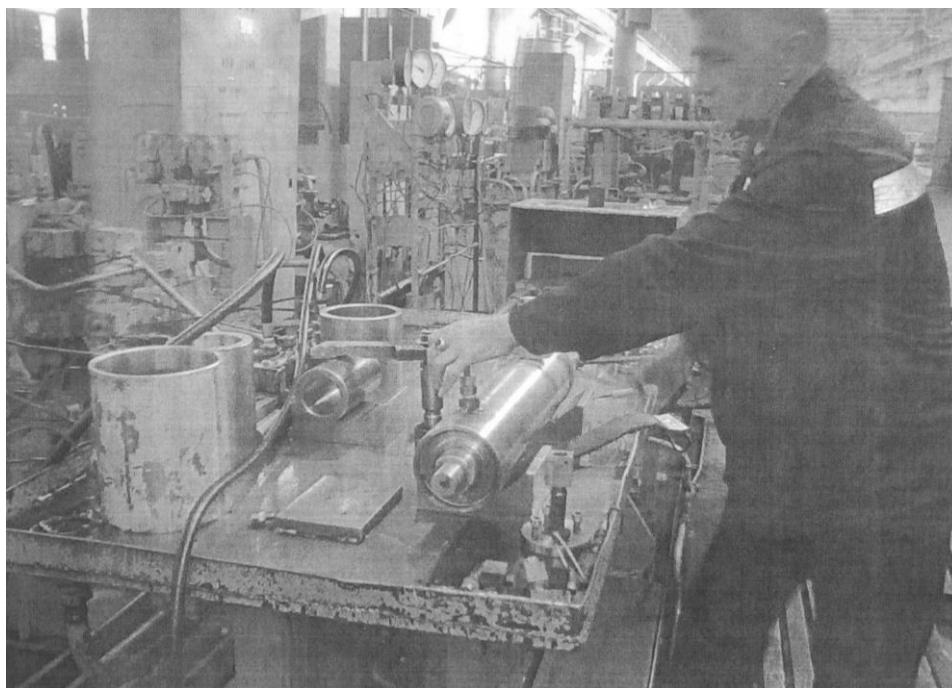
Испытание гидроцилиндра на стенде
